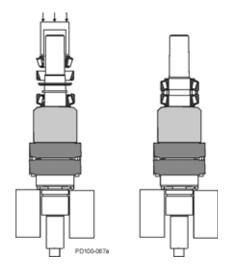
Assemblage du roulement à rouleaux coniques arrière
